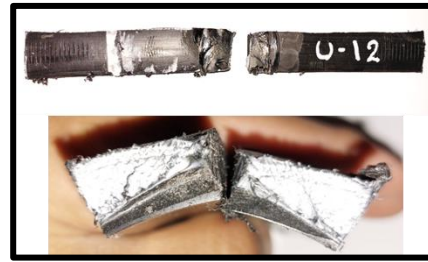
Unión tubo – tubo por extrusión sufre fractura frágil justo en la unión.
